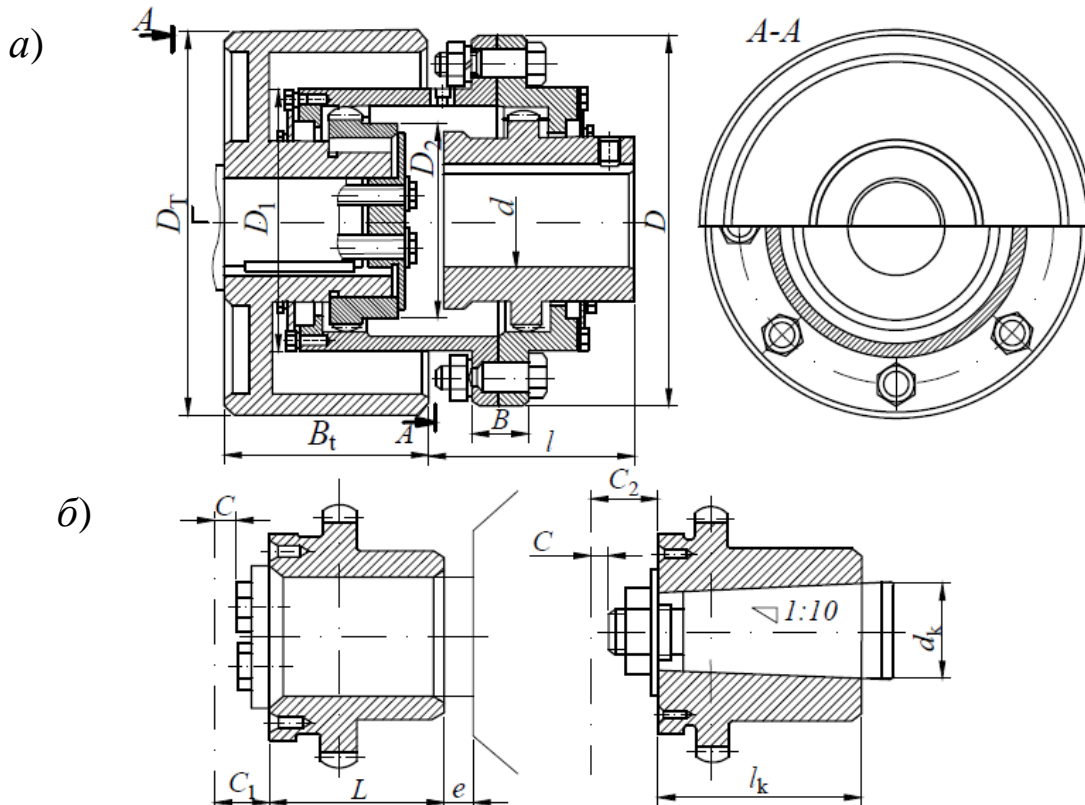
Зубчатые муфты с тормозными шкивами [24]:
